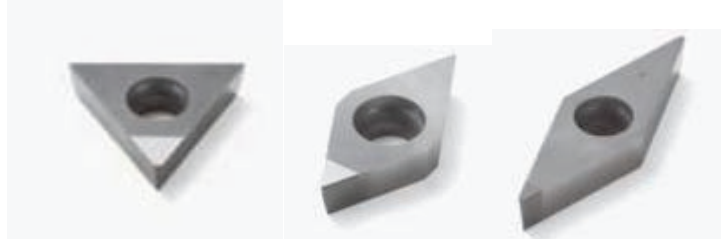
корпусные фрезы с PCD-пластинами
